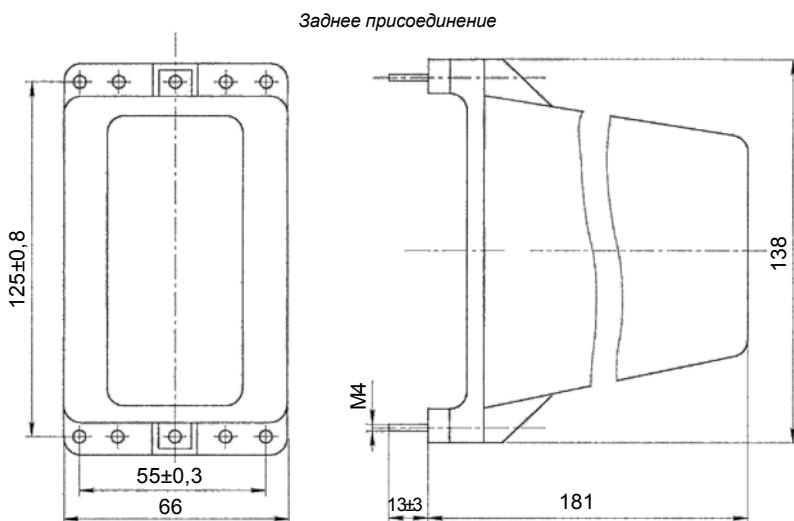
Габаритные, установочные и присоединительные размеры устройства типа КРБ-12
